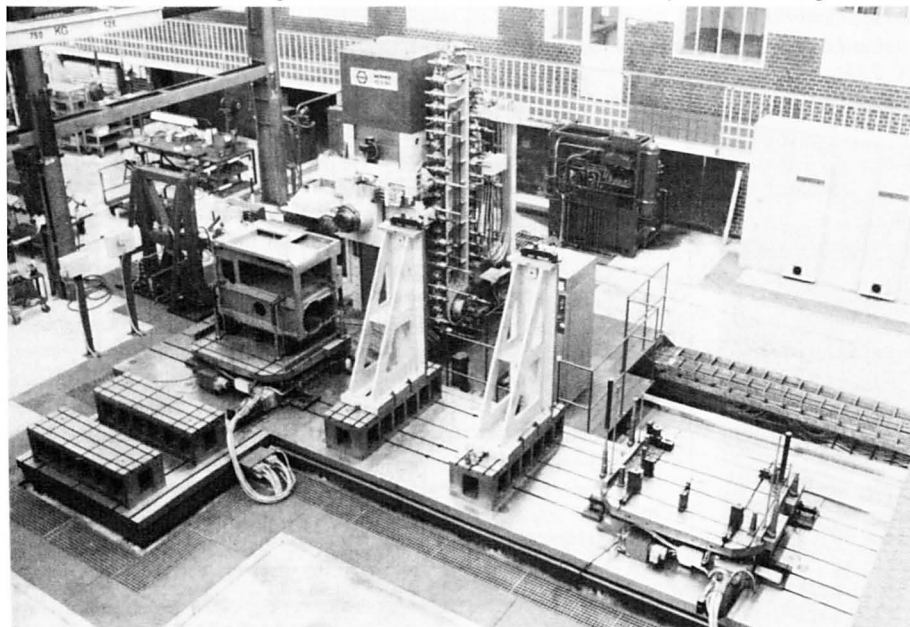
Bearbeitung eines Werkzeug-Tellermagazins gegen einen Winkel gespannt auf einem Bearbeitungszentrum «Werner TC 2 So 8»
